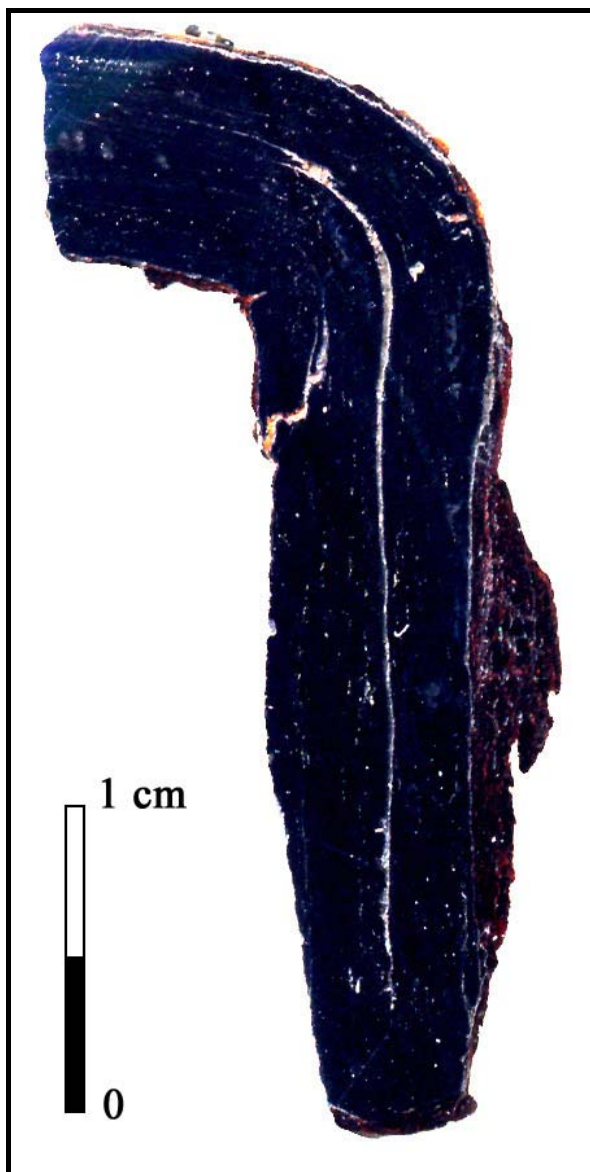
Section MAD 12a montrant une soudure centrale.
